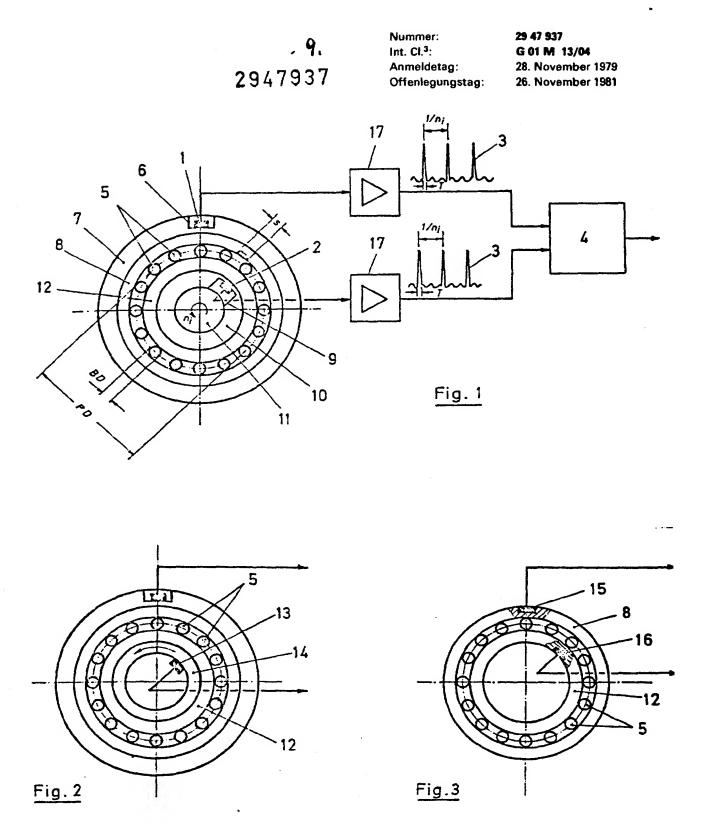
zeigt ein Schnittbild eines radial wirkender Wälzlagers. Der feststehende Außenring 8 des Lagers steht in kraftschlüssiger Verbindung mit einem Lagergehäuse 7, welches am Außendurchmesser eine Nut 6 trägt, auf deren Grund ein Dehnungsmeßstreifen 1 appliziert ist. Der Innenring 12 hat kraftschlüssige Verbindung zu einer Buchse 10 auf einer Welle 11, die sich mit der Drehzahl ni dreht. Die Buchse hat an ihrer Innenseite eine Nut 9, auf deren Grund der Dehnungsmeßstreifen 2 appliziert ist. Die Meßsignale 3 des inneren Dehnungsmeßstreifen 2, die z. B. über Schleifringübertrager nach außen geführt werden und die Meßsignale 3 des äußeren Dehnungsmeßstreifen 1 werden mittels Verstärker 17 und einer Auswerteelektronik 4 weiterverarbeitet. Die Auswerteelektronik ermittelt den Schadensort und die Schadensgröße nach der vorher b zeichneten Formel I.
